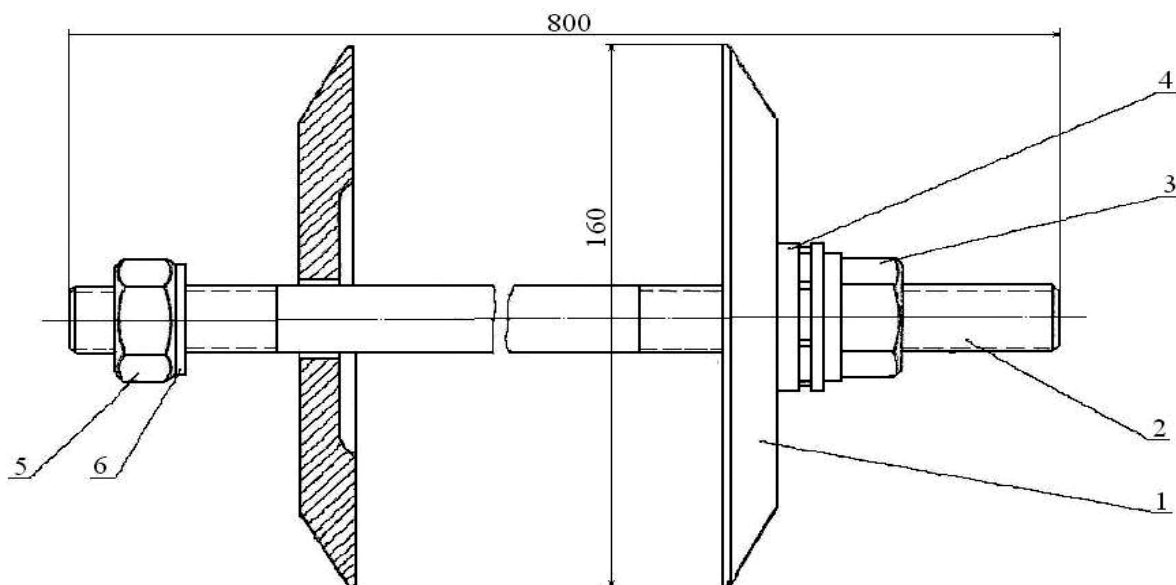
Приспособление для запрессовки втулок под подшипник СД 7859 – 4004
